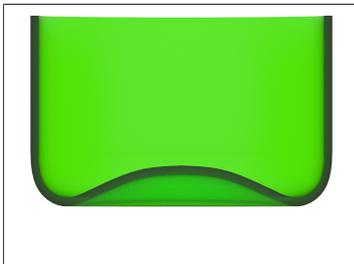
Schnittbild einer Flasche mit einer leichten Hohlkehle
